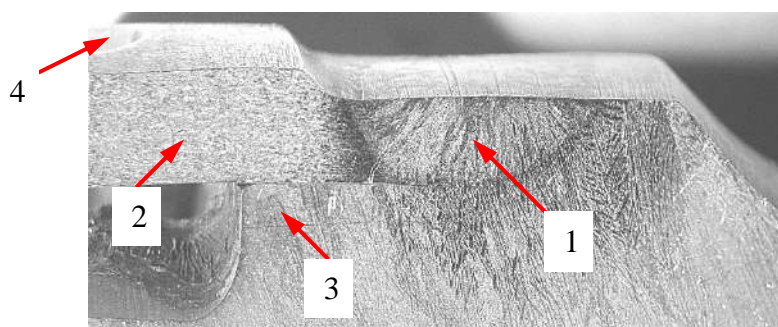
2 Макроизображение сечения форсунки на участке сварного шва. Стрелками показаны: 1 – сварной шов, 2 – пруток Ø 24, 3 – пруток Ø 17, 4 – отверстие окислителя. Увеличено.
